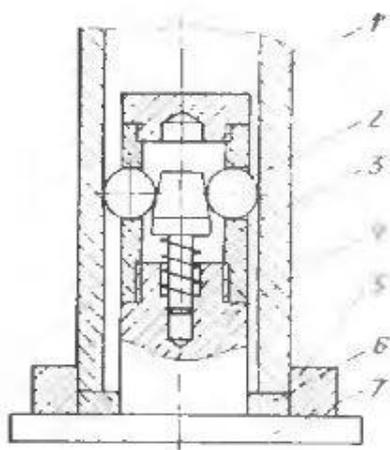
Приспособление для автоматического центрирования трубы относительно фланца
